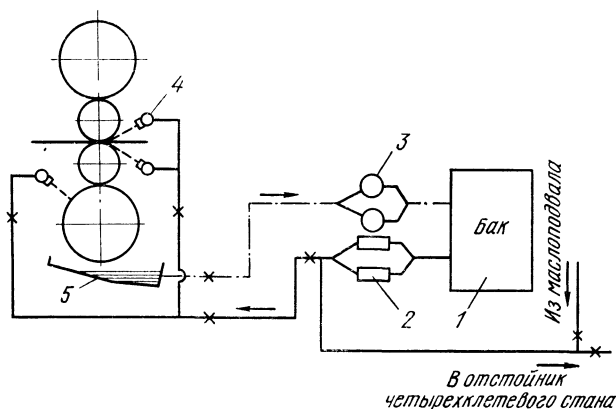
Схема установки для подачи эмульсии на дрессировочном стане 1700 Череповецкого металлургического завода:
